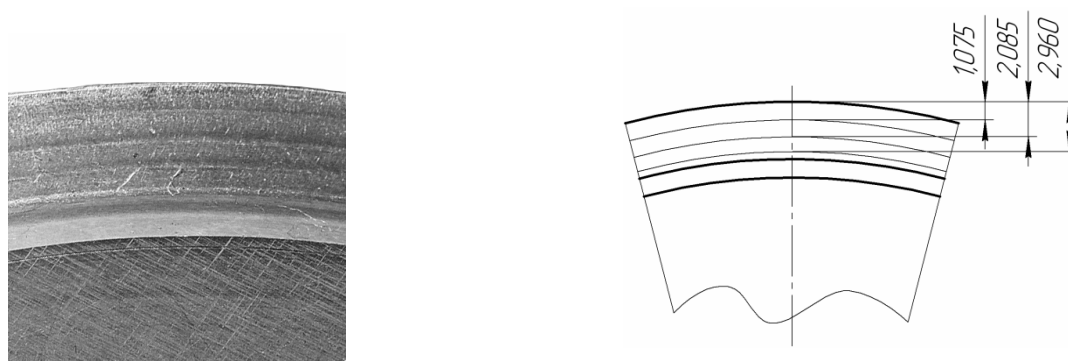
Схема расположения концентрических окружностей по боковой поверхности деформирующего инструмента
